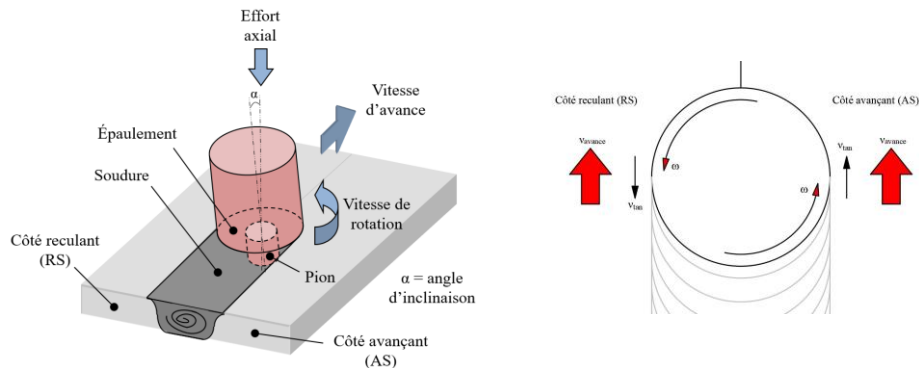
Représentation du soudage par friction malaxage
